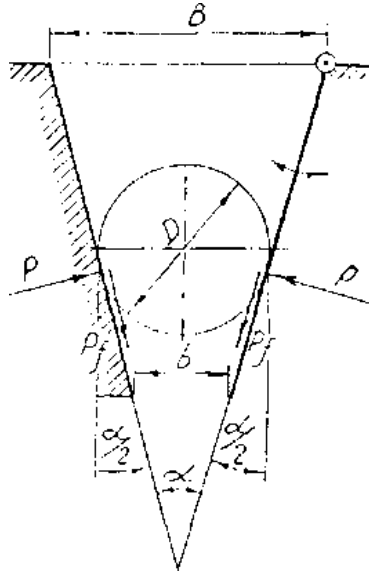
Розрахункова схема щоквої дробарки.
